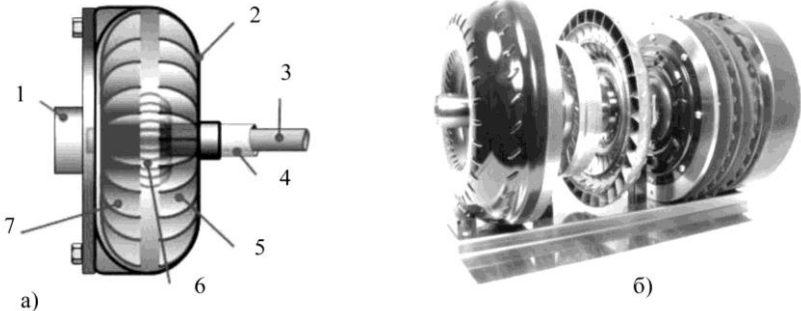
Внешний вид автоматической коробки передач.
